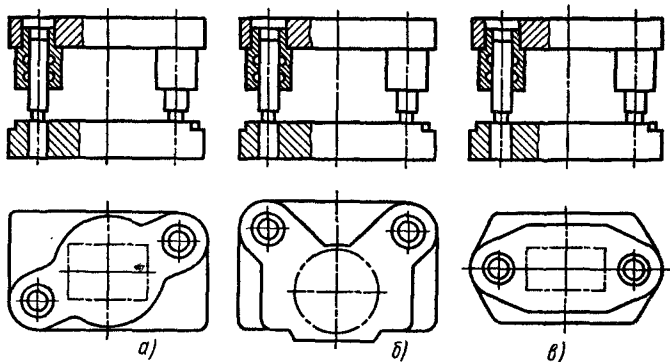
Стандартные блоки штампов с расположением колонок:
